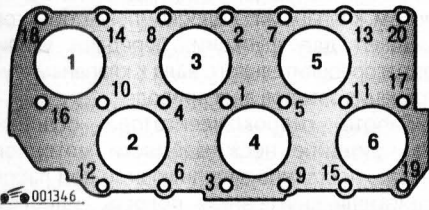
Последовательность затяжки болтов крепления головки блока цилиндров
